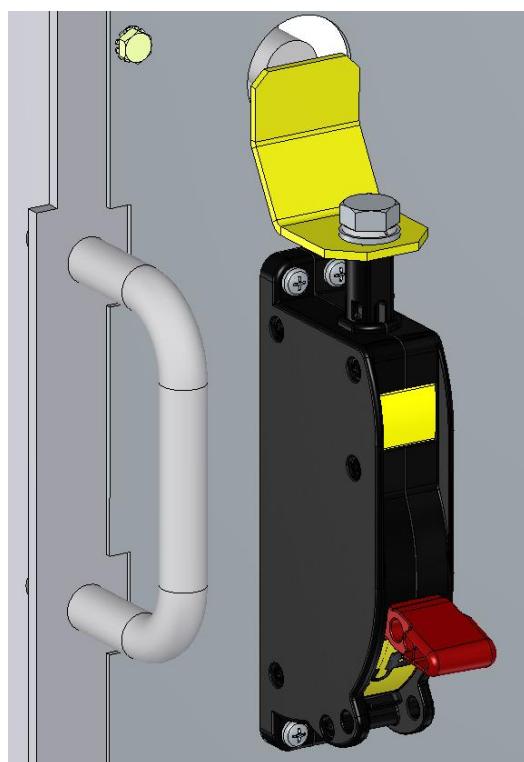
Блокиратор закрывающий доступ к червячному редуктору
